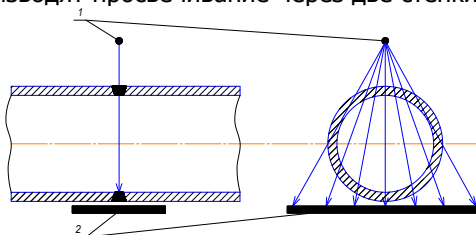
Схема фронтального просвечивания через две стенки за одну установку источника без его смещения относительно сварного шва:
